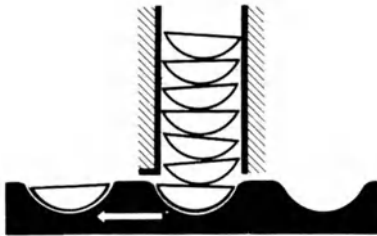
Kuppelnde Vorrichtung wie in Abb. 465 u. 466 arbeitet ohne Beschädigung.
